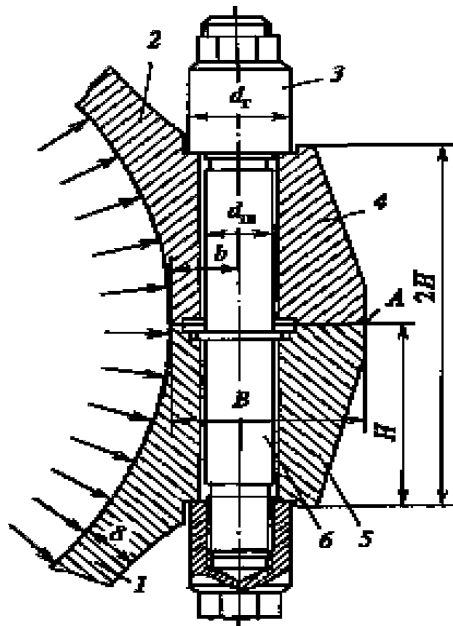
Схема фланцевого з'єднання верхньої та нижньої половин корпуса:
